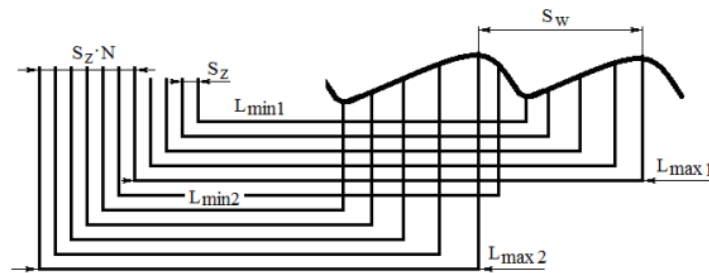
Схема визначення кроку хвилястості на обробленій поверхні після попутного фрезерування
